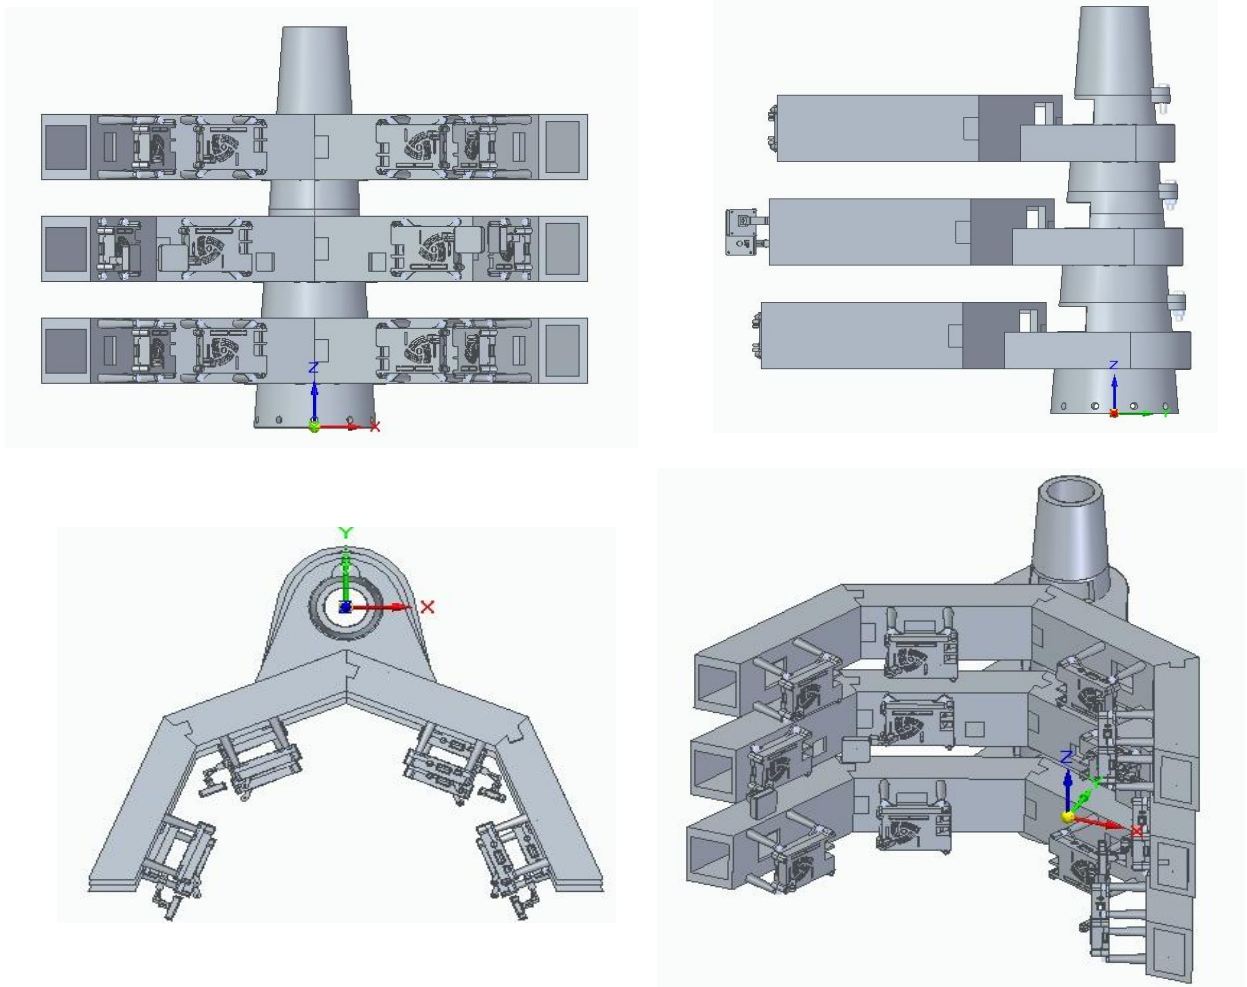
Alzado, planta, perfil y vista 3D de la cuarta versión de la estructura.
